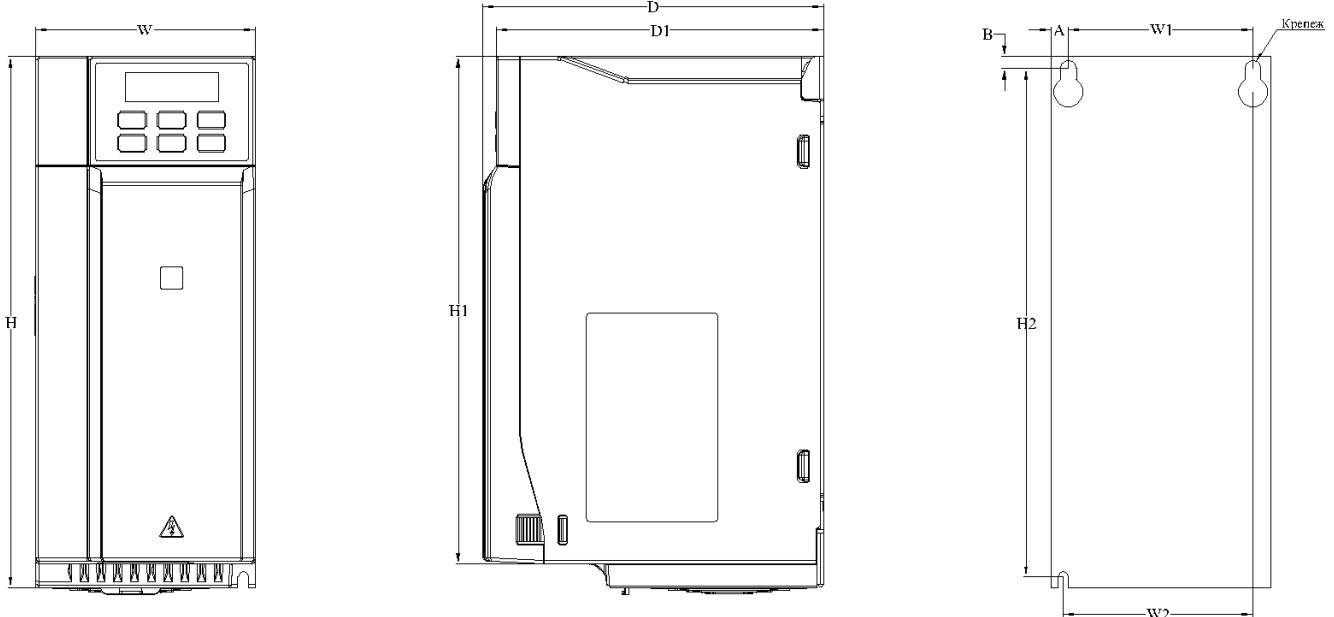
Чертеж преобразователя частоты типоразмер 2
